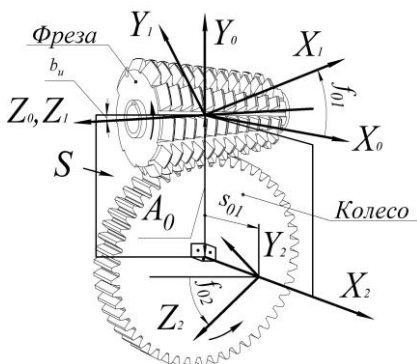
Розрахункова схема формоутворення косозубих зубчастих коліс черв'ячними фрезами
